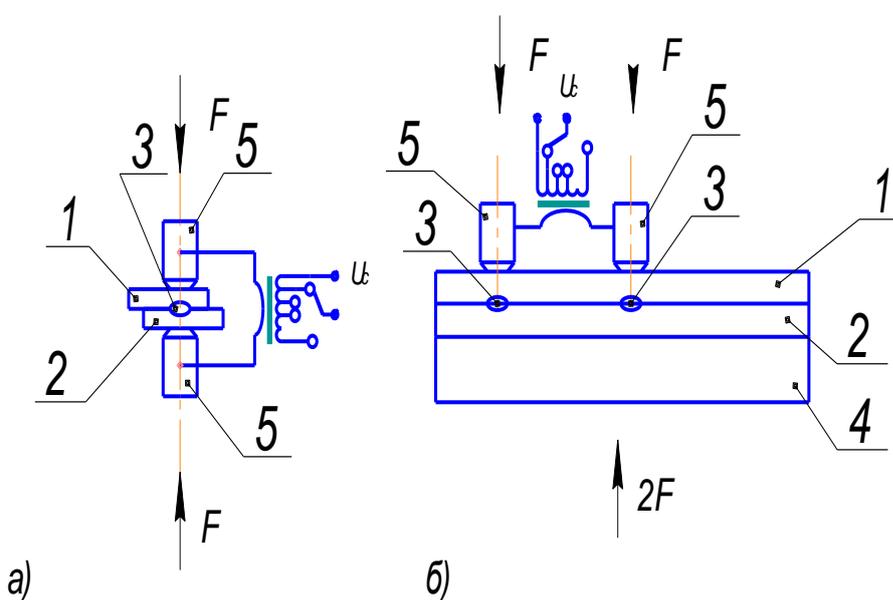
Схема процесса контактной точечной сварки:
